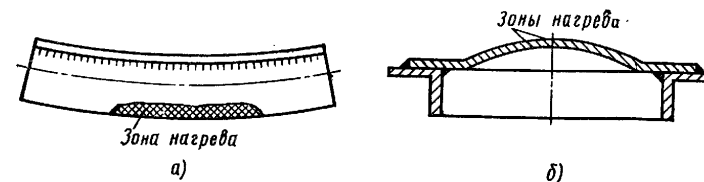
Схемы расположения зон нагрева при термической правке различных конструкций:
